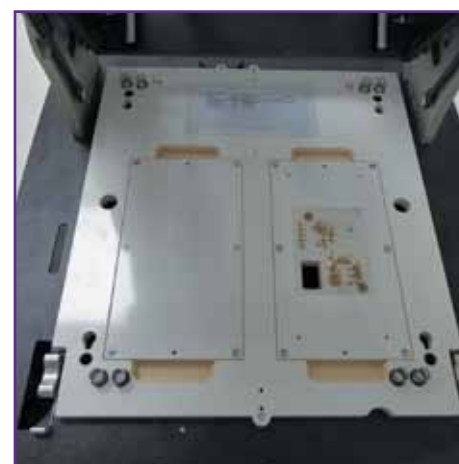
MMI-B. Нижняя неподвижная пластина для установки тестовых щупов
